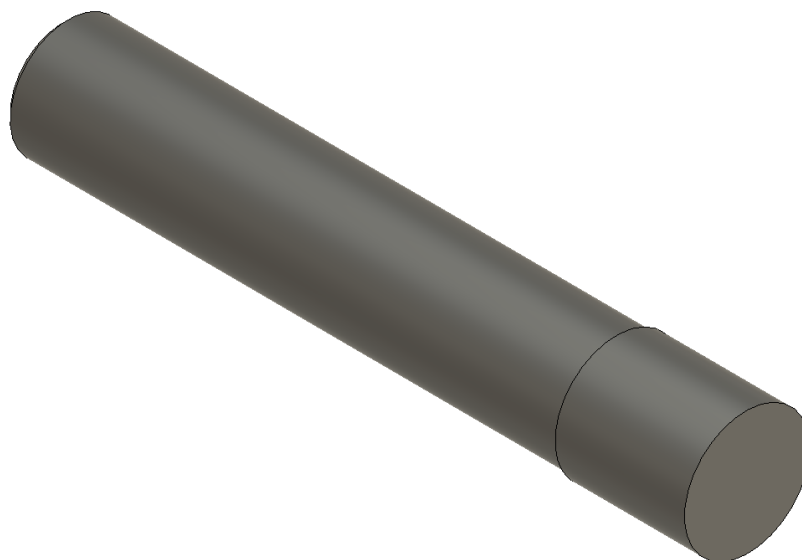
Вигляд заготовки на операцію 020 Токарна з ЧПК
